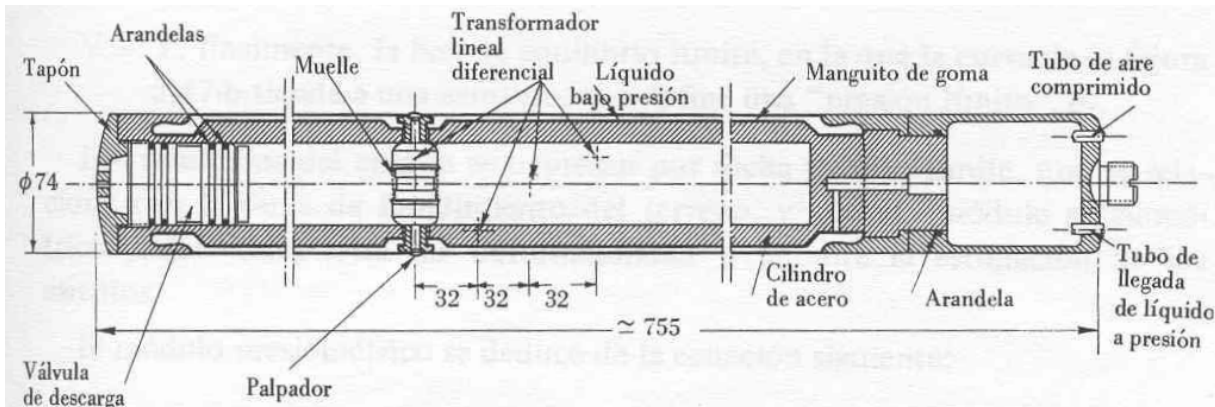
Dilatómetro para roca del laboratorio de Ingeniería Civil de Lisboa (Candacho 2009).
